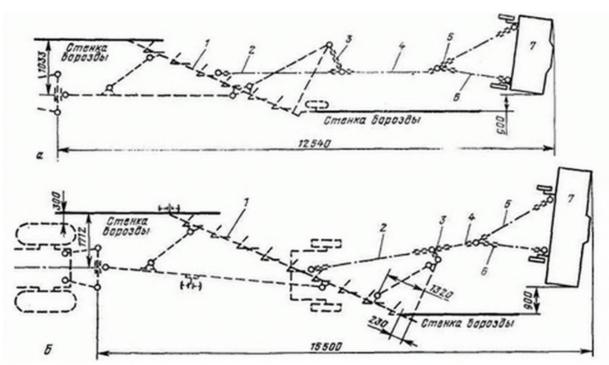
Схема присоединения приспособления ПВР-2,3 к пяти-, шестикорпусному плугу (a) и приспособления ПВР-3,5 к плугу ПТК-9.35 (б): 1 - плуг; 2 – цепь; 1 = 3.6 (для ПТК-9-35 1 = 4...4,5м); 3 – цепь; 1 = 1,26м; 4 – цепь 1 = 1,4м; 5 – цепь 1 = 2,5м; 6 – цепь 1 = 2,15м; 7 – приспособление.
